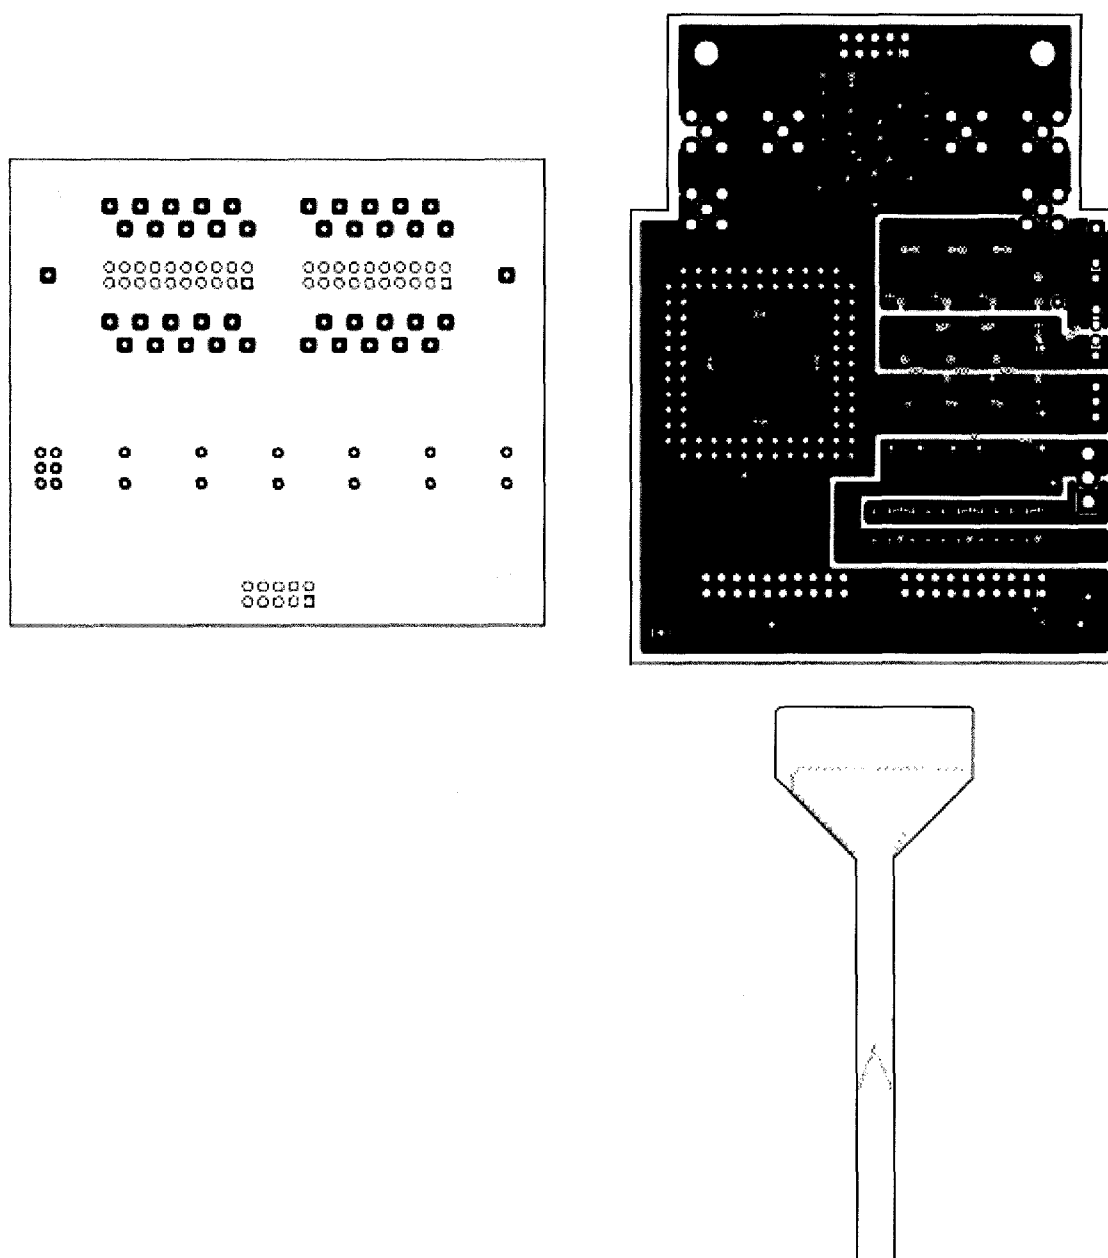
Le dessin de masque du circuit imprimé (vue milieu, couche d'alimentation).
